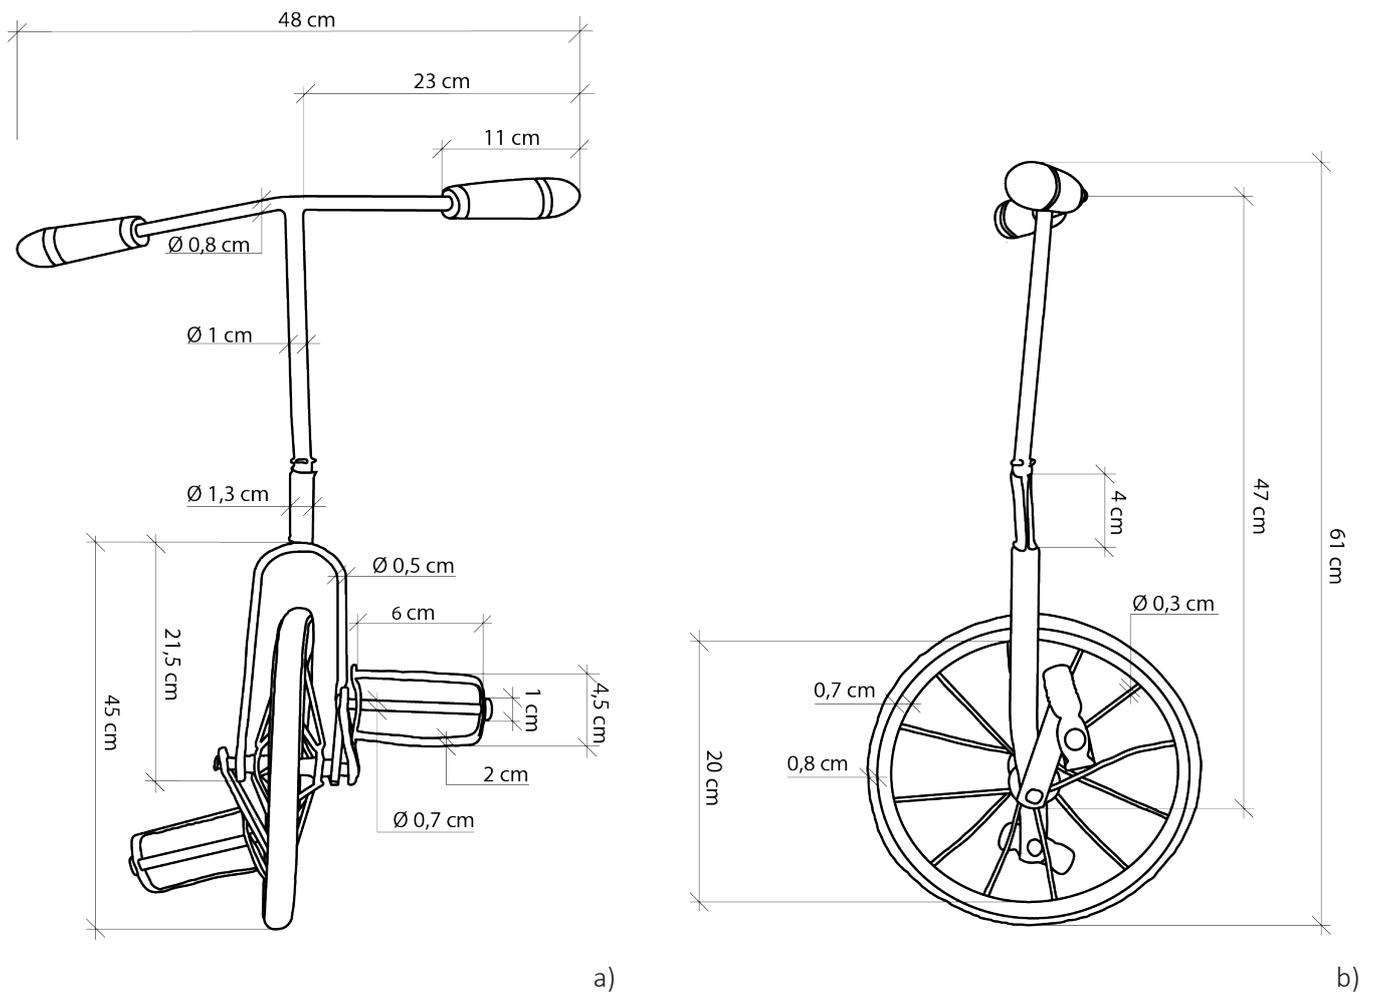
Dibujos técnicos (a-b). a) Dibujo técnico alzado; b) Dibujo técnico perfil.
